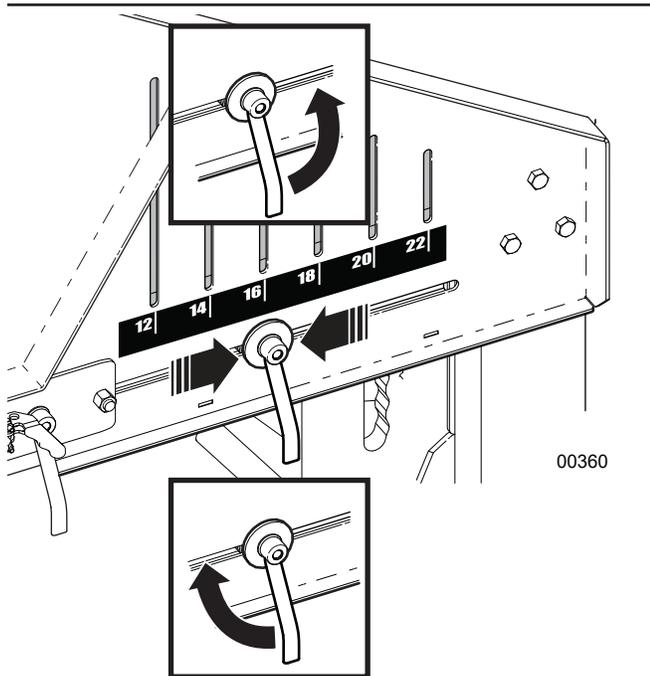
Poignée de verrouillage du guide de butée des grumes
